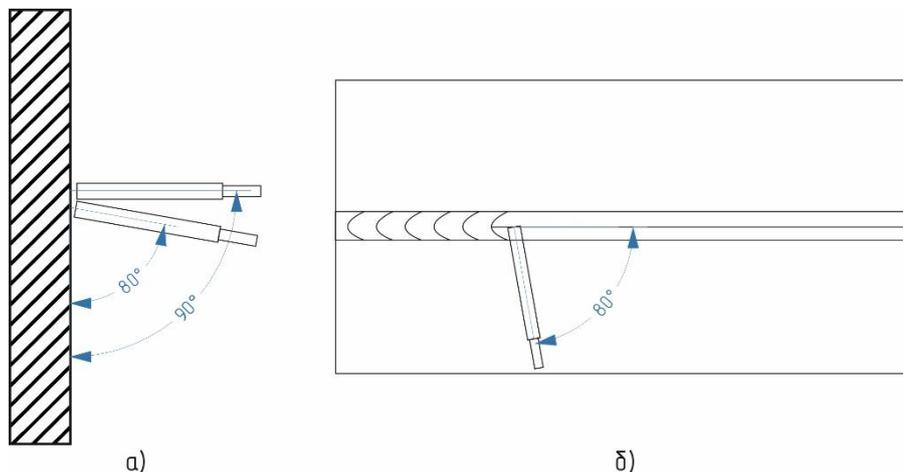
Положения электрода при сварке в горизонтальном положении: а) – относительно вертикальной плоскости детали; б) – относительно направления сварки
